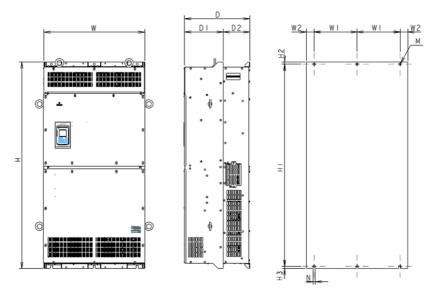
Dimensiones externas del variador (FRN220AQ1S-4□ a FRN400AQ1S-4□)
